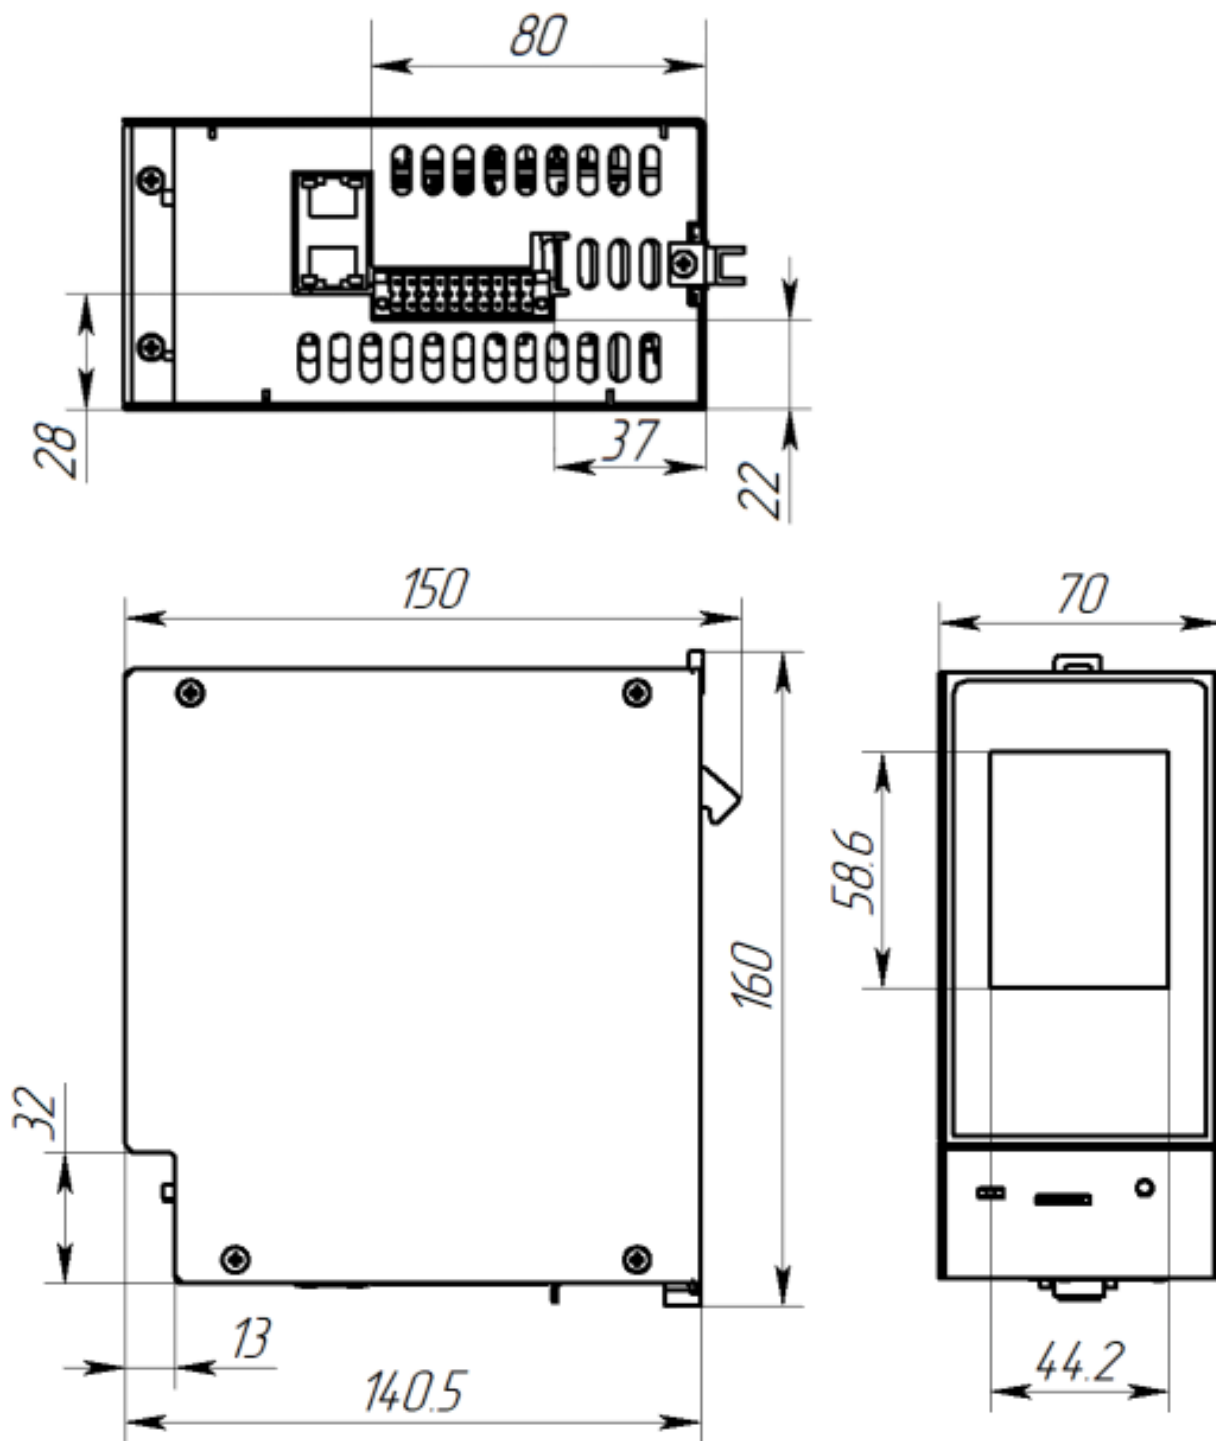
Габаритные и присоединительные размеры модуля ЦПУ в металлическом корпусе
